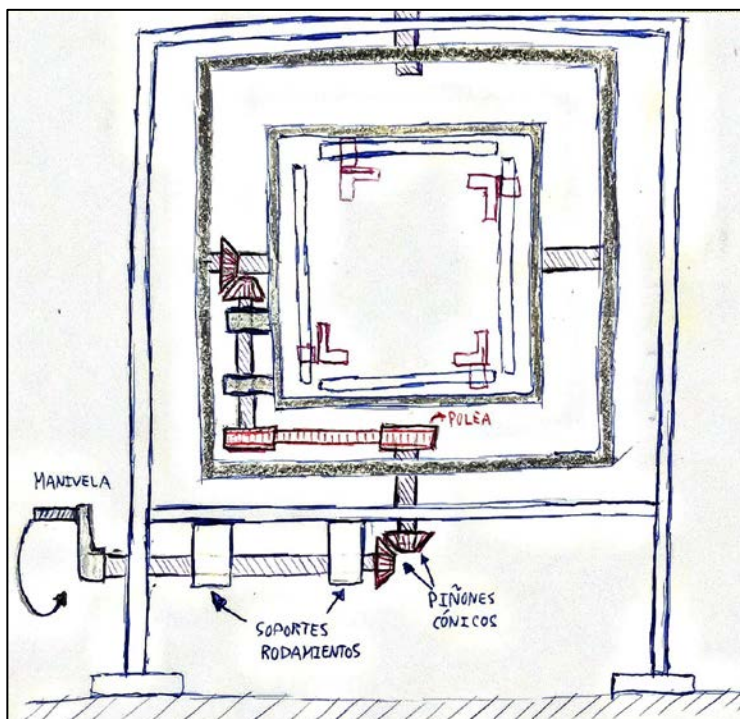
Alternativa 2. Estructura de tableros de aglomerado con sistema de accionamiento y sistema de anclaje.
